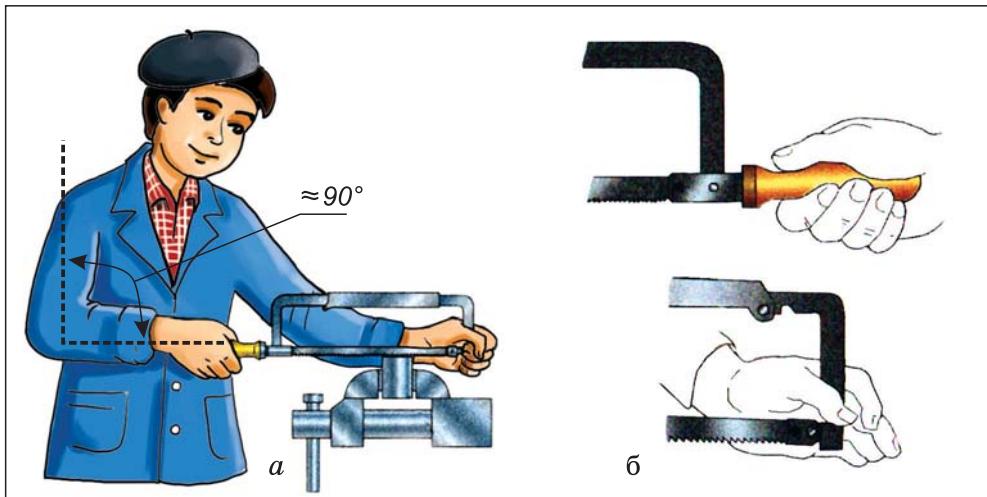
Работа ножовкой: а) – положение корпуса; б) – положение рук
